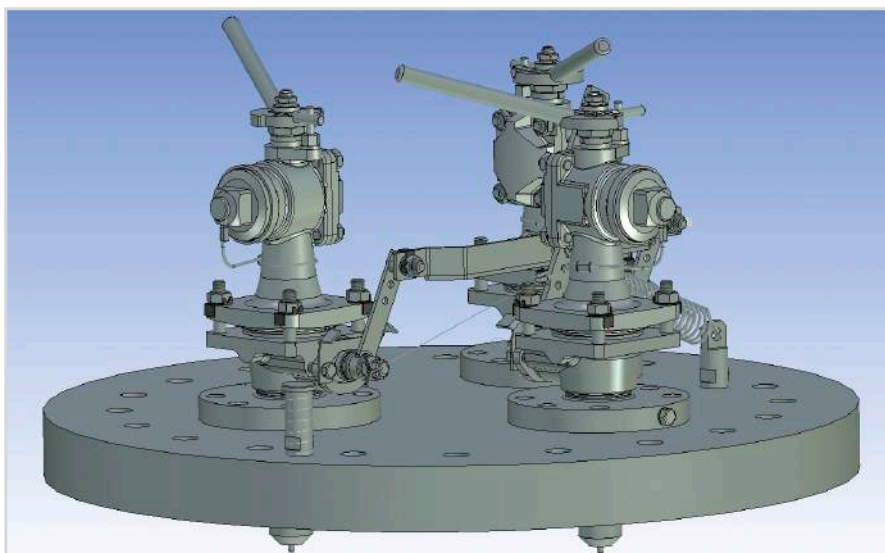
3D-модель установки устройств слива и налива на крышке люка
